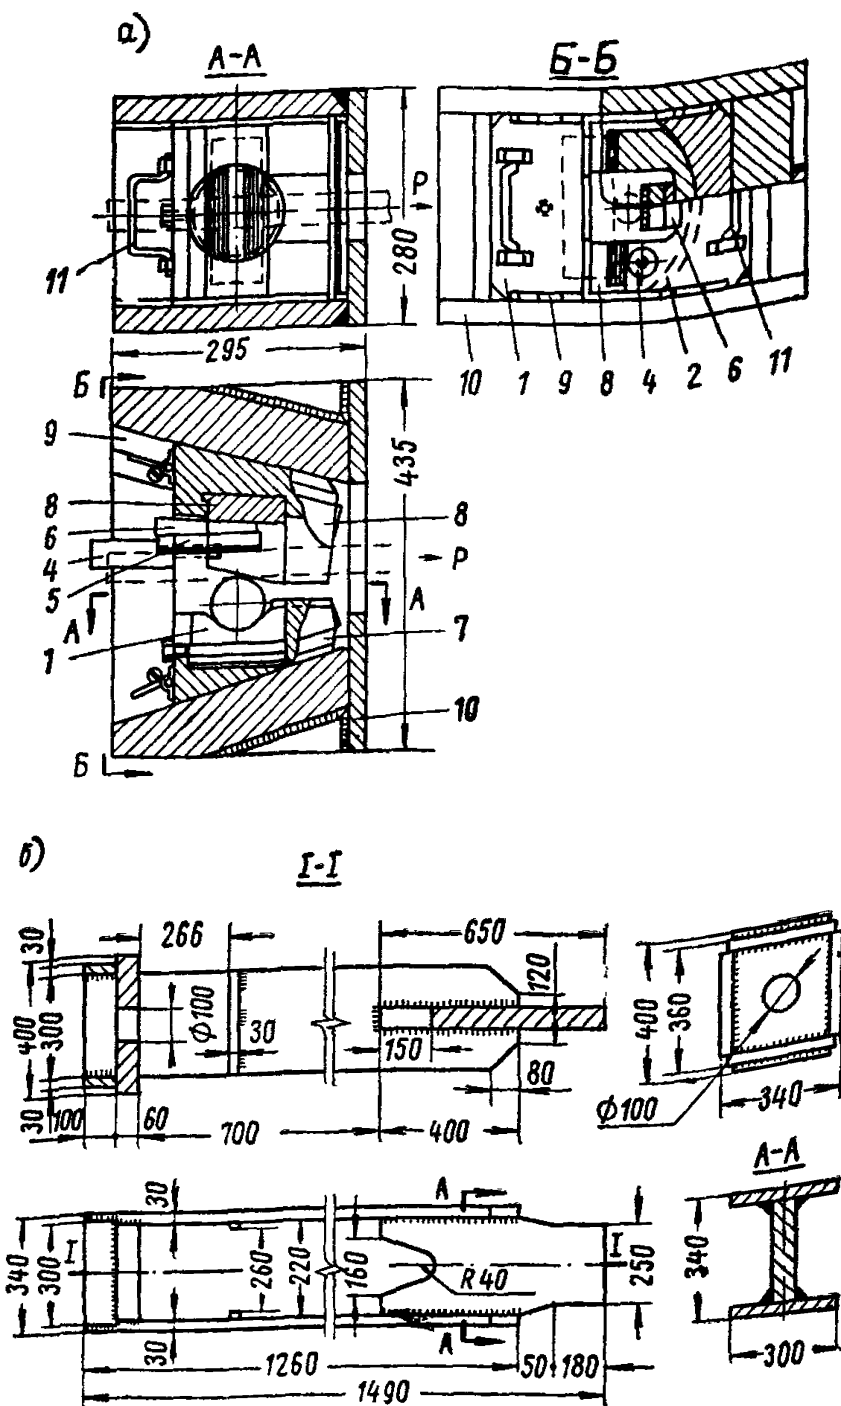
Конструкция приспособления для испытания на прочность образцов сварных крестообразных соединений двух пересекающихся стержней с помощью горизонтальных испытательных машин
